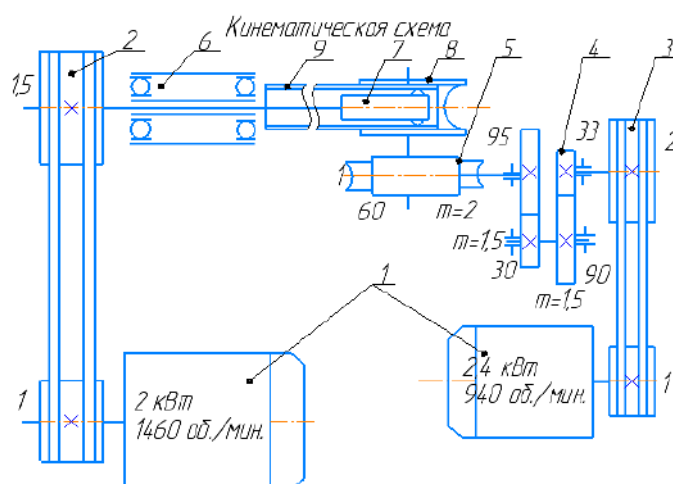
Кинематическая схема станка для холодной гибки труб методом раскатывания:
